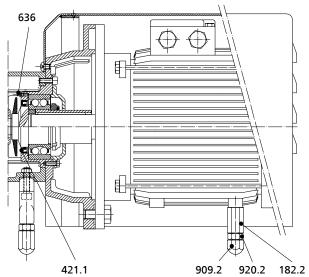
Сборочный чертеж, типоразмер двигателя IEC 132-180
